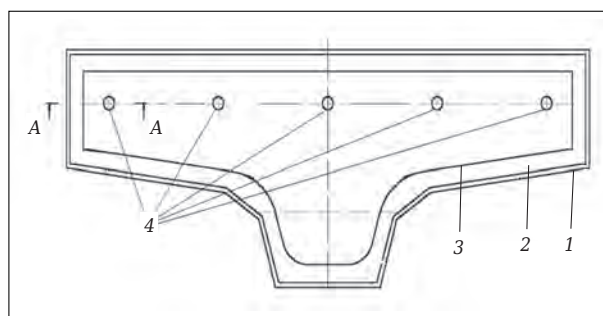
Компоновка ПК: 1 – корпус; 2 – футеровка; 3 – дно ПК; 4 – разливочные отверстия
